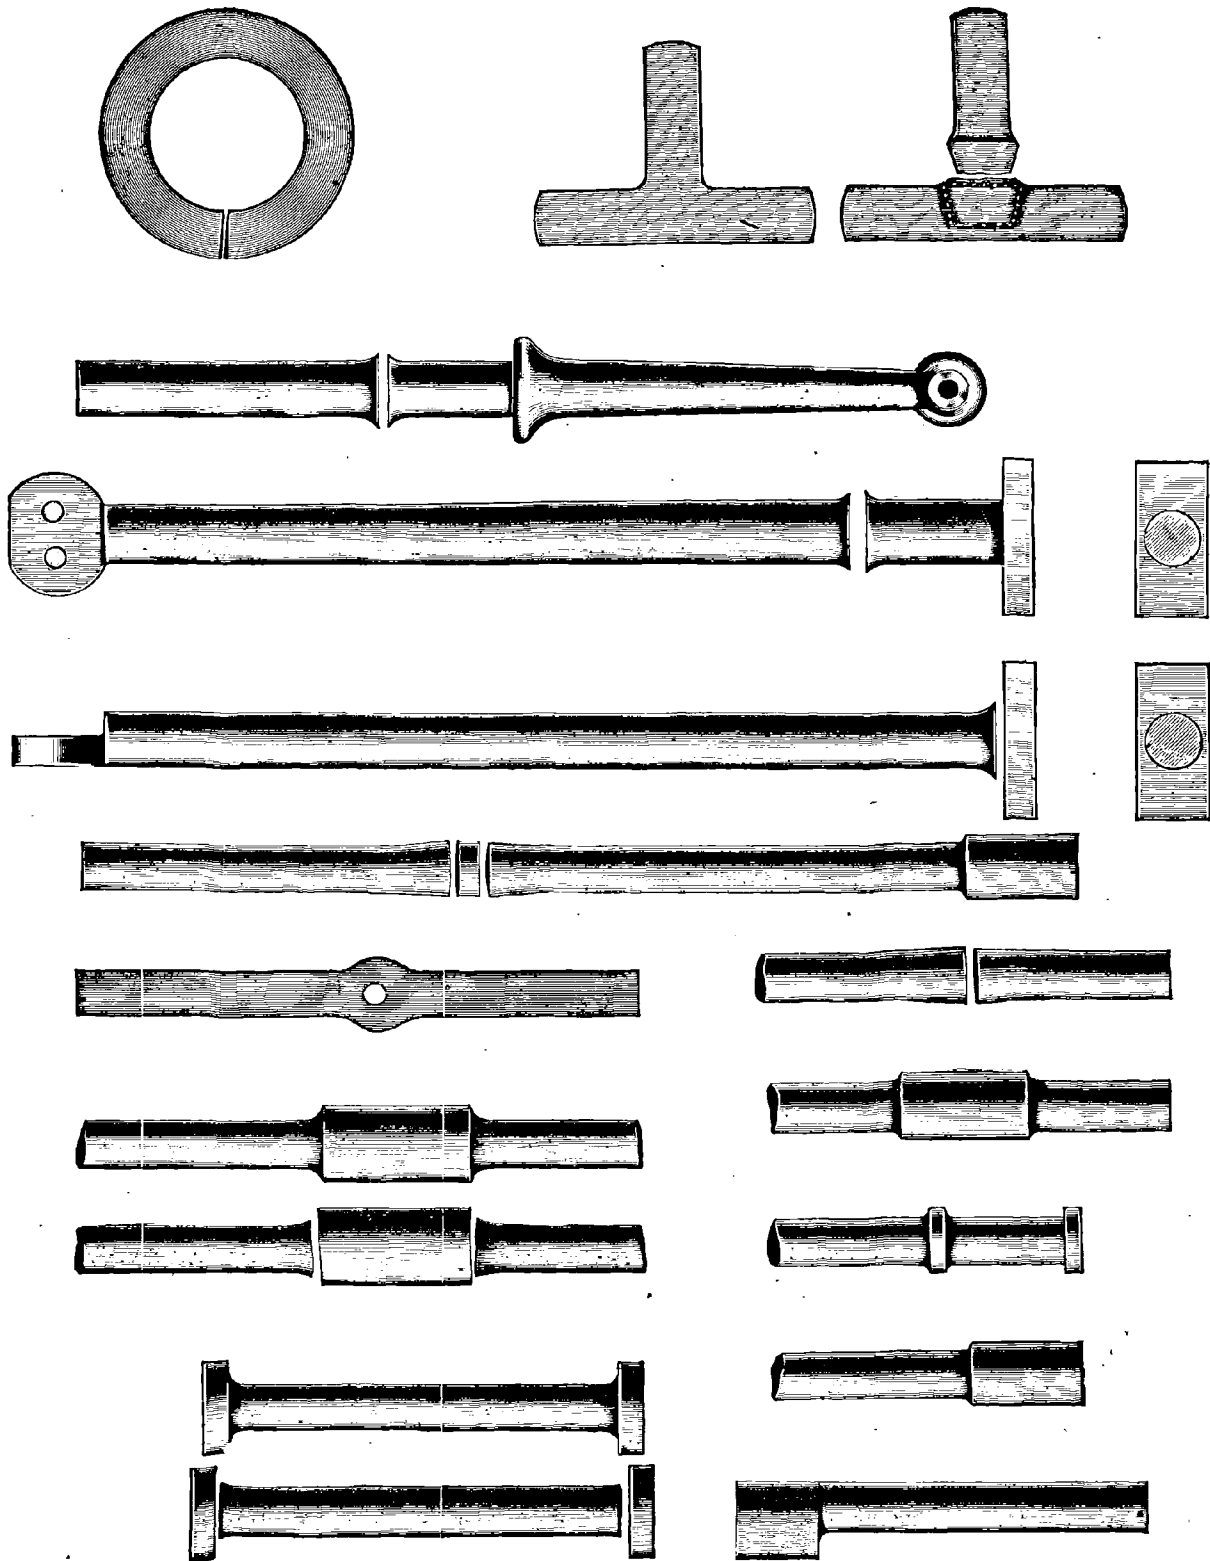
Pièces de forges obtenues avec la machine à forger et à souder Debombourg.
